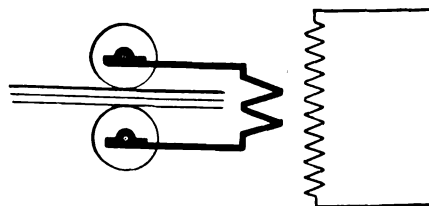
Principe de la soudure continue sous molettes.
